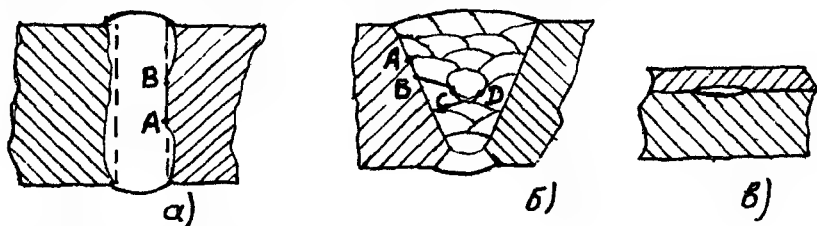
Сварные соединения с несплавлениями
